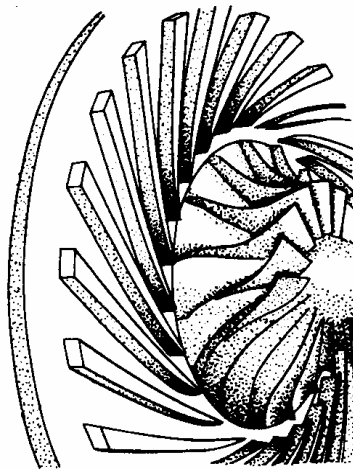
Рабочее колесо и каналный диффузор сверхзвуковой центробежной ступени
